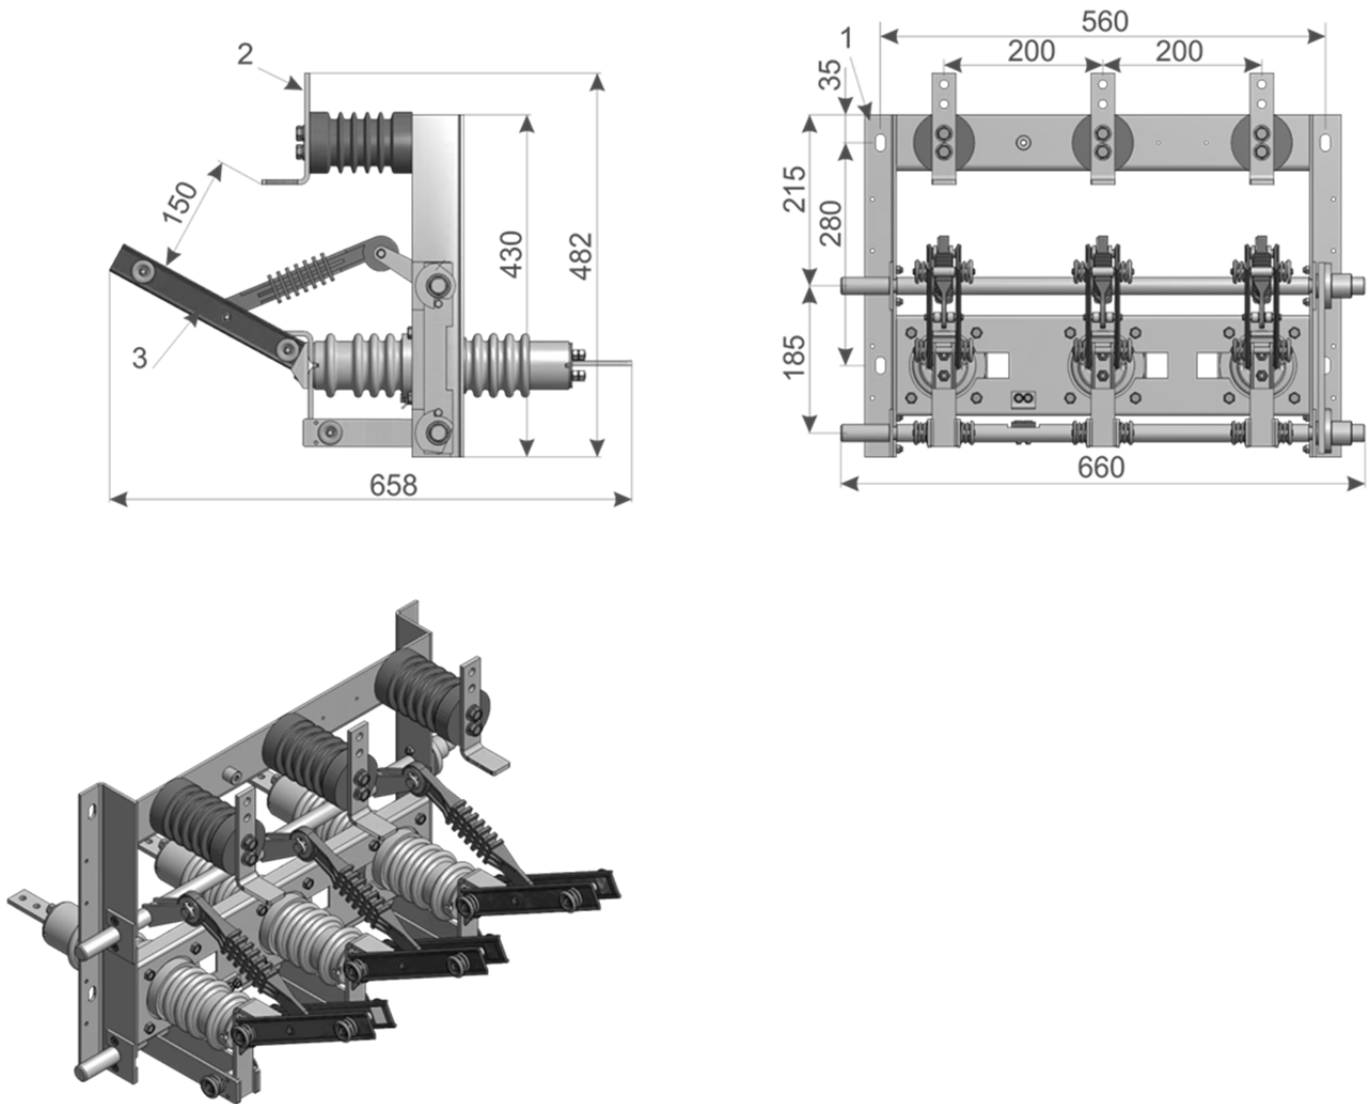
Габаритно-установочные размеры и устройство разъединителя РВФЗ
